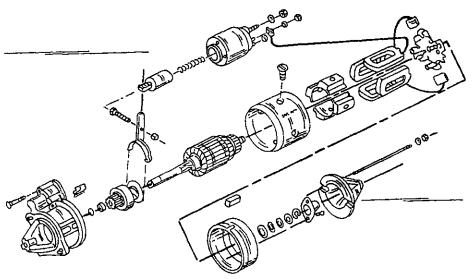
Монтажный чертеж стартера фирмы Bosch.
